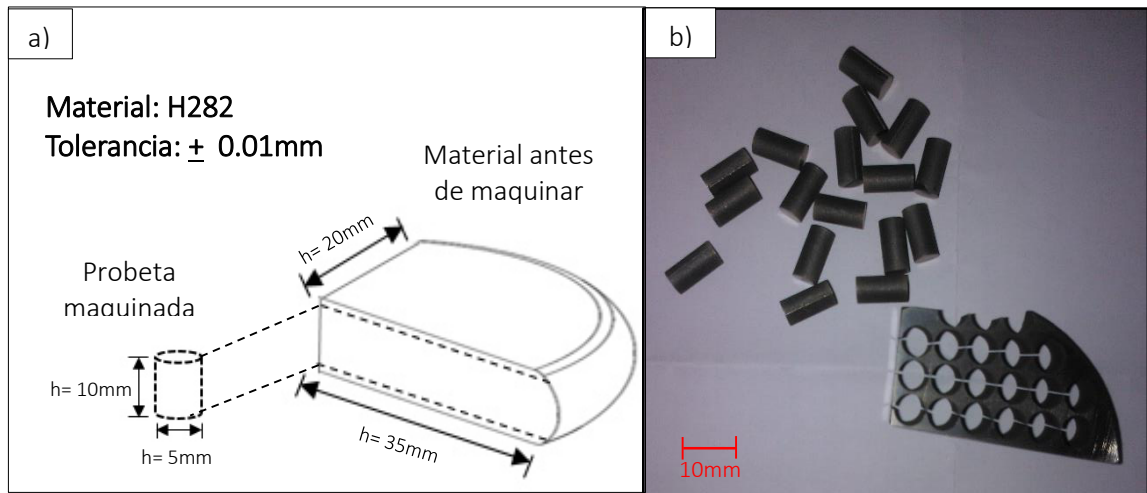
a) Dimensiones de las probetas y del material antes de ser maquinado, b) Imagen real de las probetas después de ser maquinadas.
